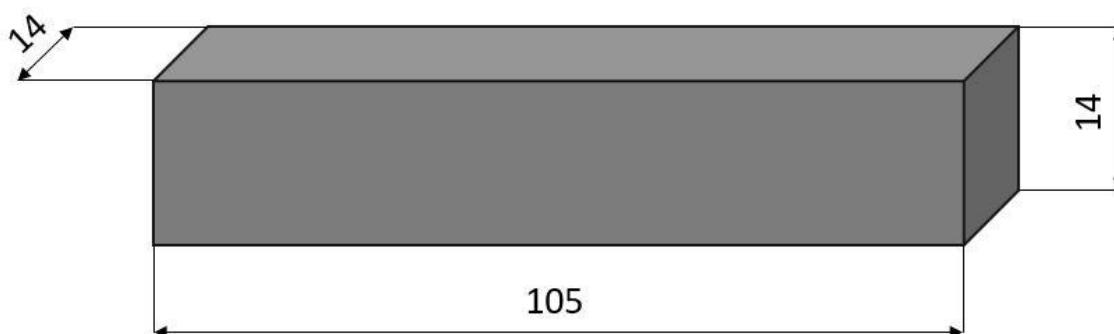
Dimensiones de la pieza a ensayar protocolo preliminar.
